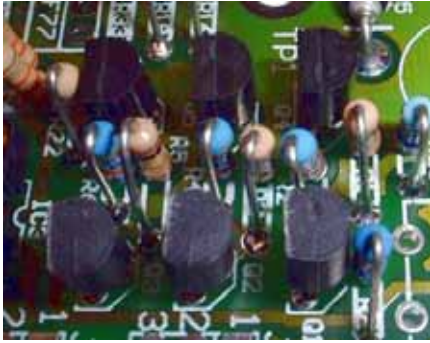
Detailansicht einiger stehend eingelöteter Widerstände und Transistoren
